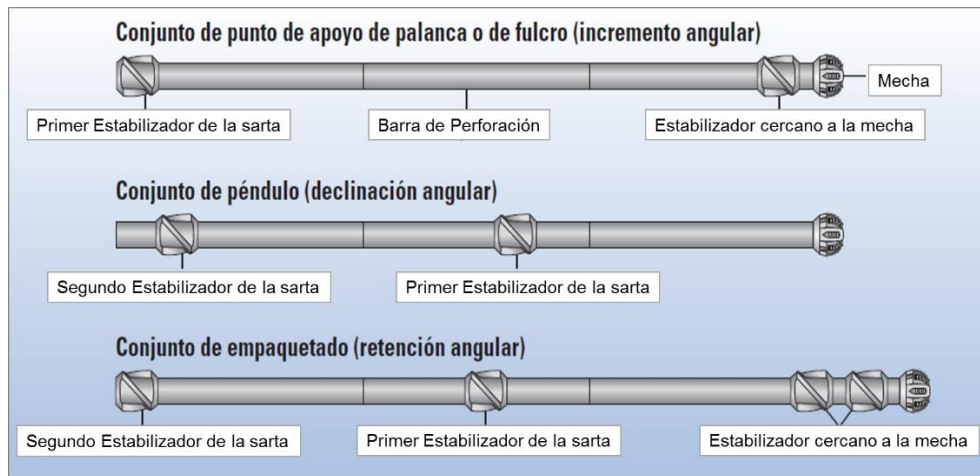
Tipos de ensamblajes de fondo ^[4]. Modificado
